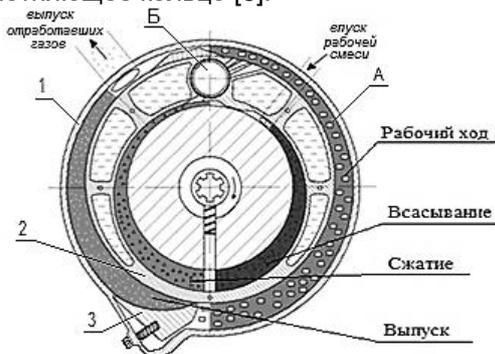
Общая схема работы роторного двигателя РДТ (первый вариант)
